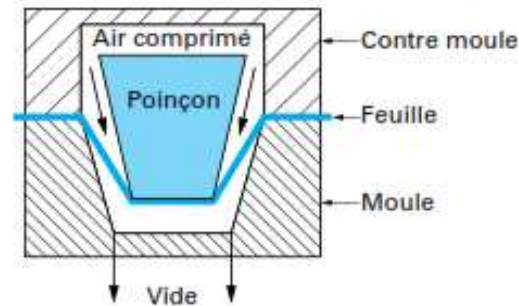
Schéma d'une machine de thermoformage à moule positif.
